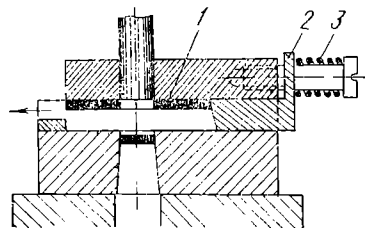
Схема пружинного сбрасывателя отштампованных деталей и отходов
